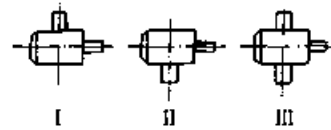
PWU型减速器外形尺寸及装配型式 (整体式)
